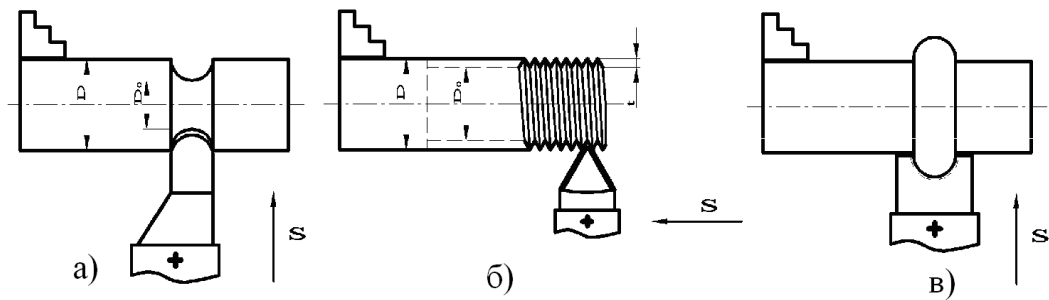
Токарні різці: а – галтельний; б - різьбовий; в – фасонний
